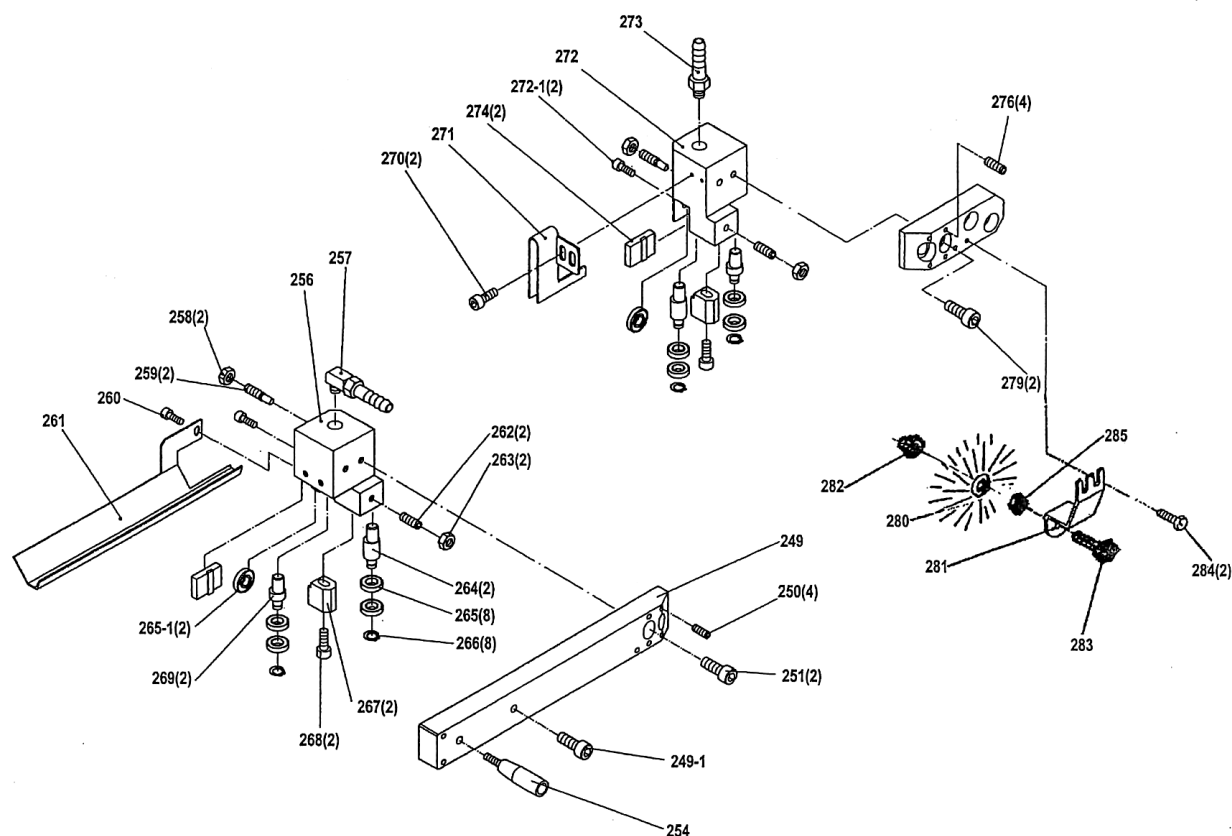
Vista explodida: guias da fita e grupo hidráulico
